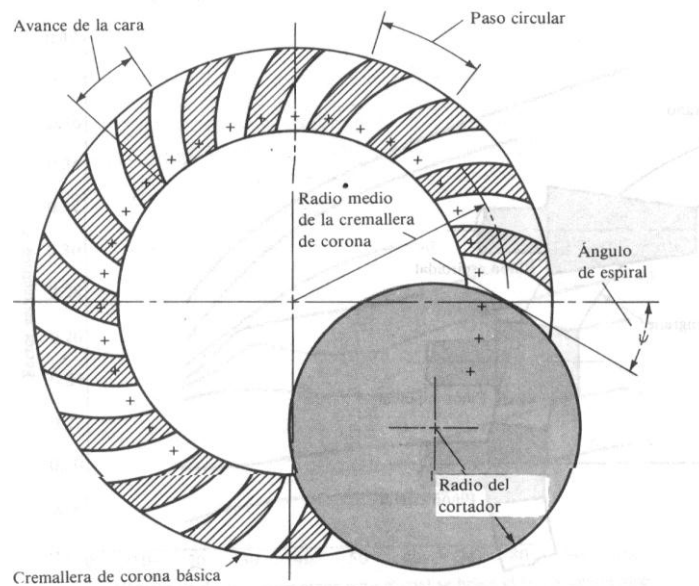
Corte de los dientes de un engrane espiral sobre la cremallera de corona básica.
